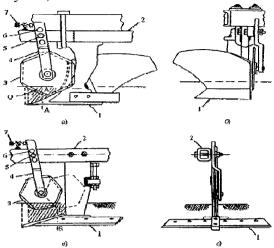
Рабочий корпус плуга (а, б) и плоскореза (в, г): а, в — вид слева; б, г — вид спереди
